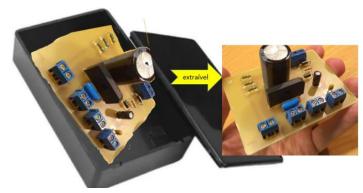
Ilustração mostrando o requisito de que a placa deve ser extraível da caixa plástica.
